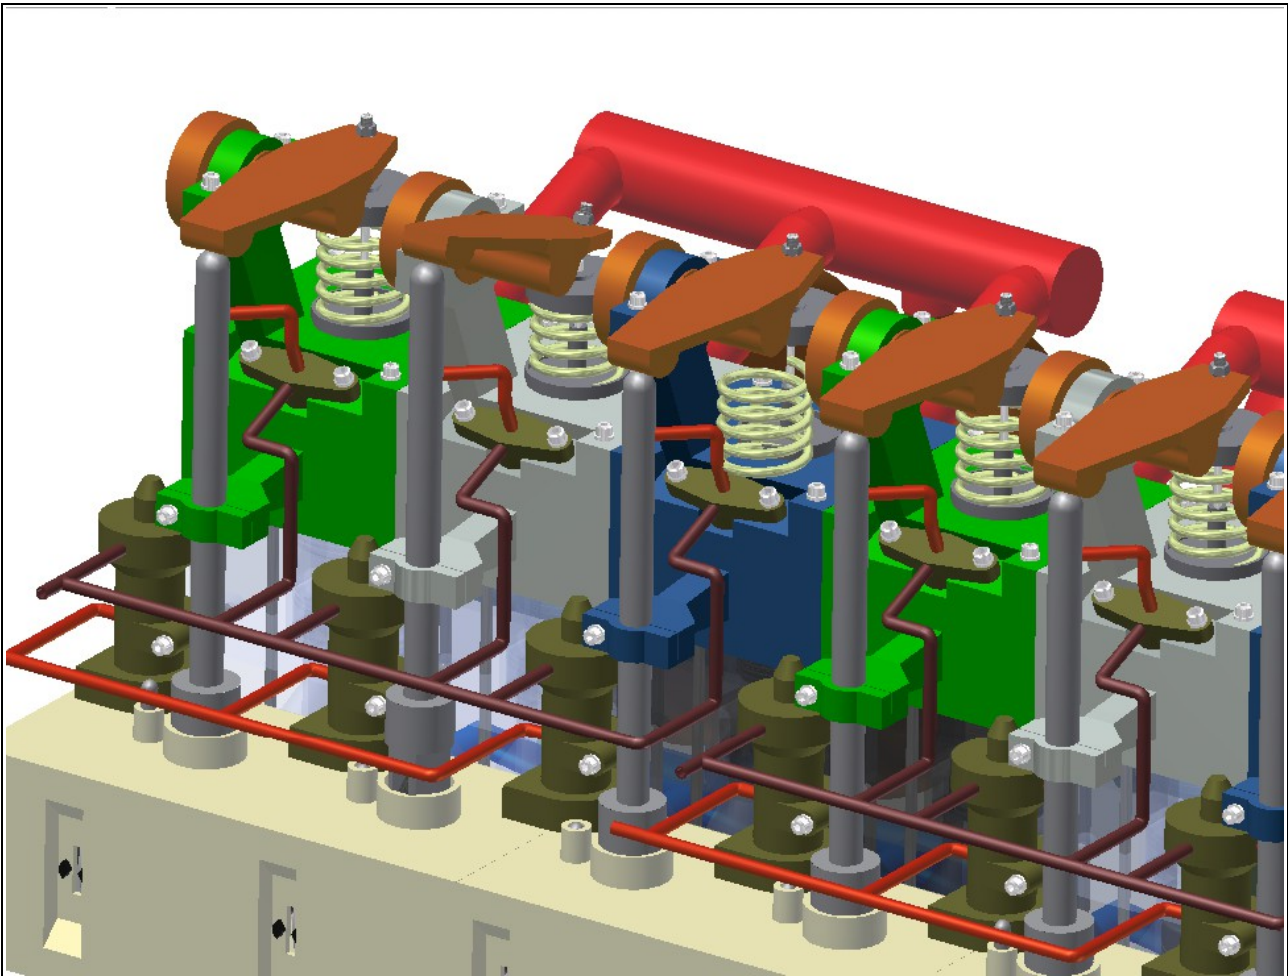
Sistema de combustible con motor, ensamble
